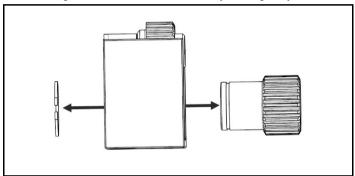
Quitar el anillo de retención del engranaje impulsor y el engranaje impulsor
